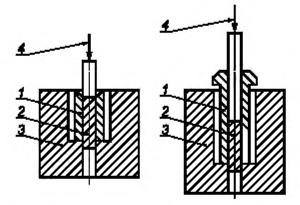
Заготовка для проверки силы удержания износостойкого элемента в корпусе шипа
